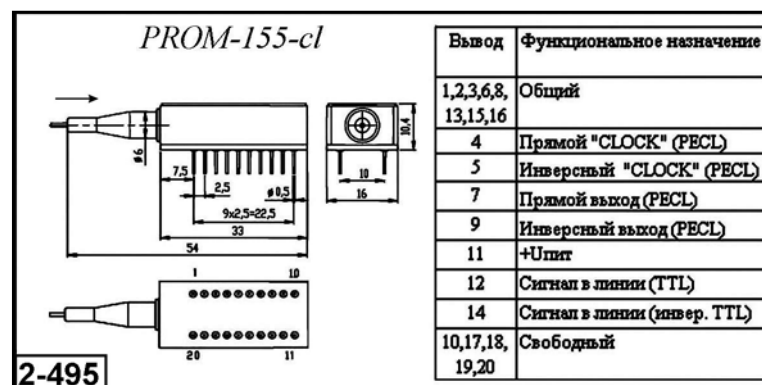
Внешний вид и габаритные размеры модуля PROM-155-cl
